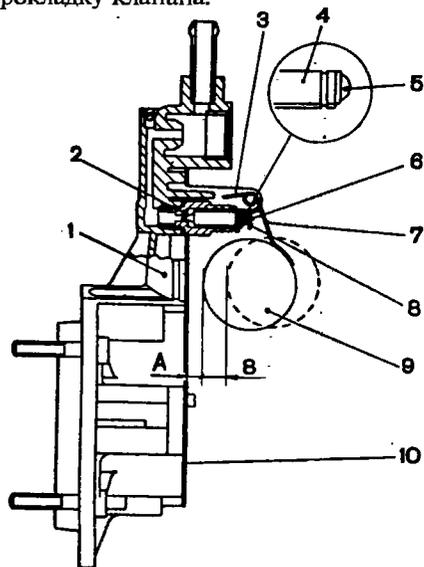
Установка уровня топлива в поплавковой камере карбюратора: 1 - крышка карбюратора; 2 - седло игольчатого клапана; 3 - упор; 4 - игольчатый клапан; 5 - шарик запорной иглы; 6 - оттяжная вилка иглы клапана; 7 - кронштейн поплавка; 8 - язычок; 9 - поплавок; 10 - прокладка
